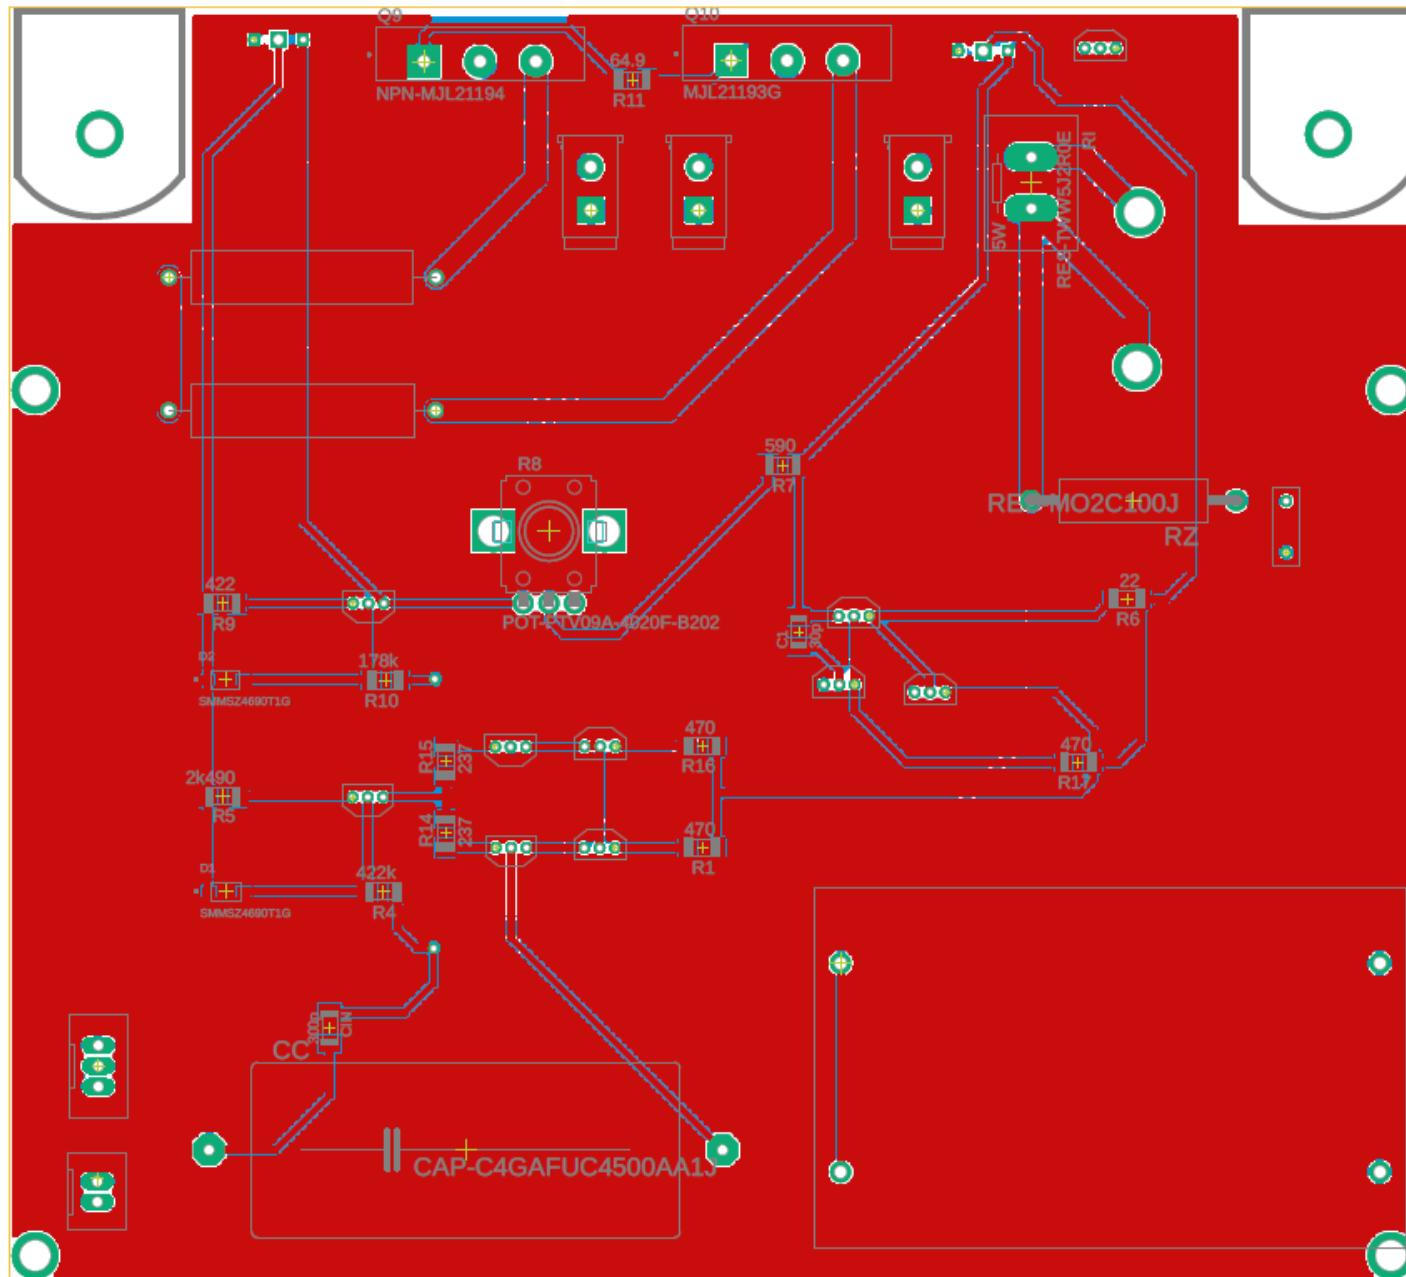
Vista de la cara superior (“Top”) de la PCB.
